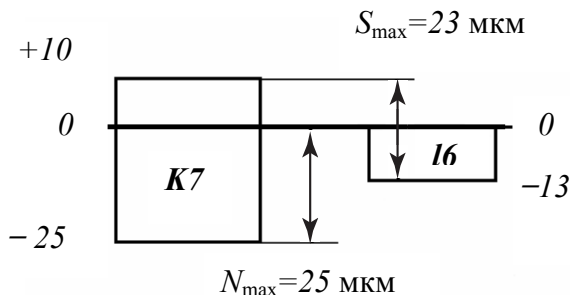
Схема расположения интервалов допусков при посадке подшипника в корпус
